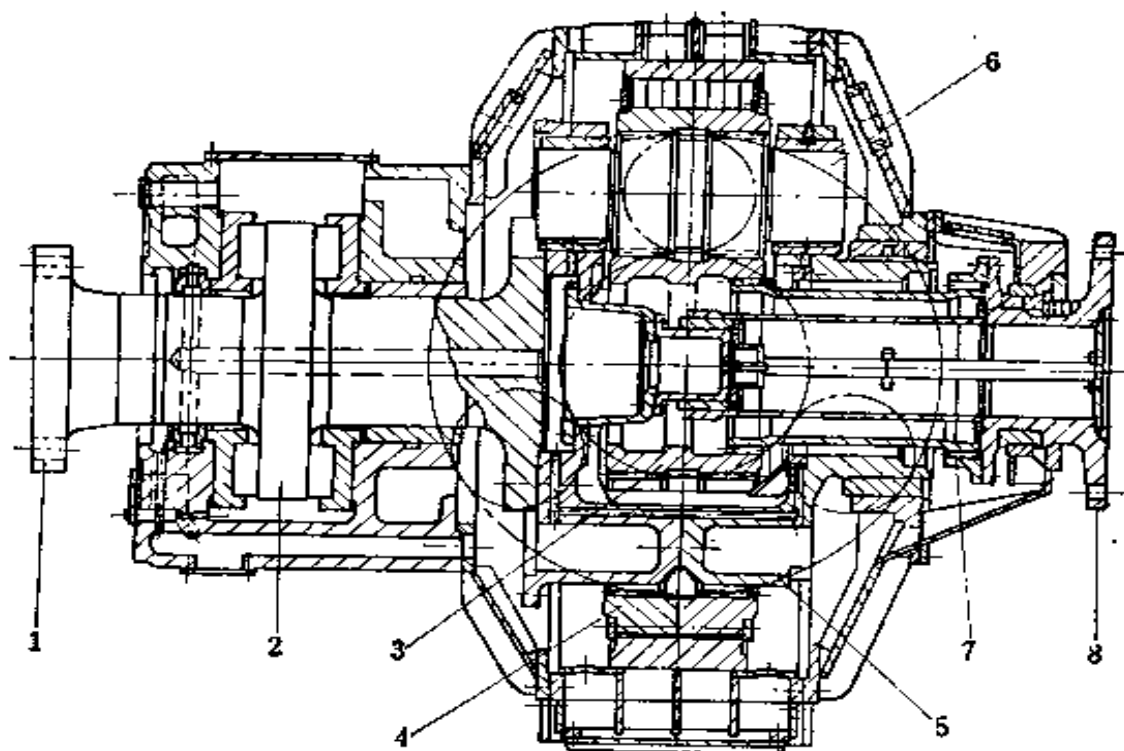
Renk 17500PS 船用行星齿轮传动箱
